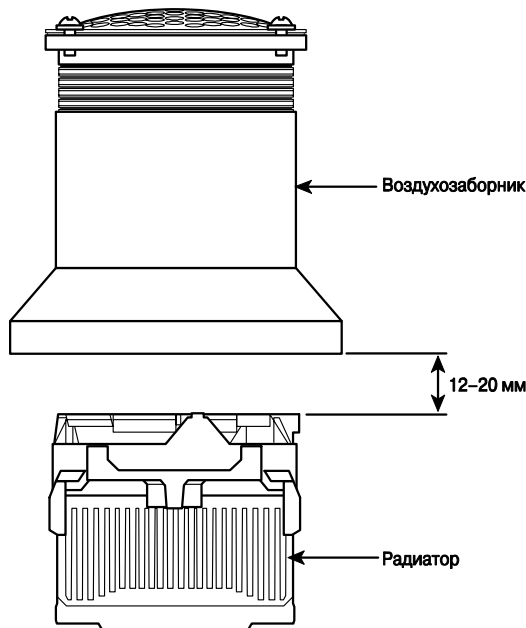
Расположение воздухозаборника относительно радиатора, установленного на процессоре
